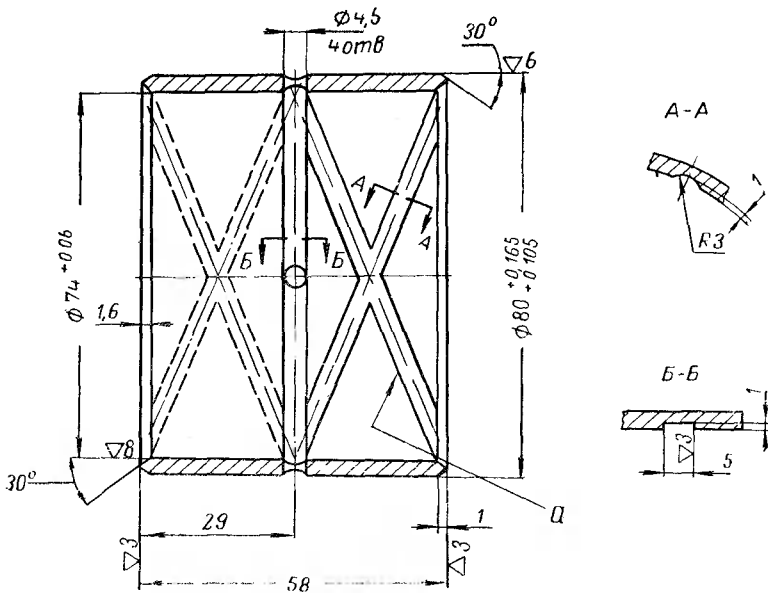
Втулка шестерен низшей и высшей передач промежуточного вала раздаточной коробки автомобилей КраЗ (214Б-1802094):
